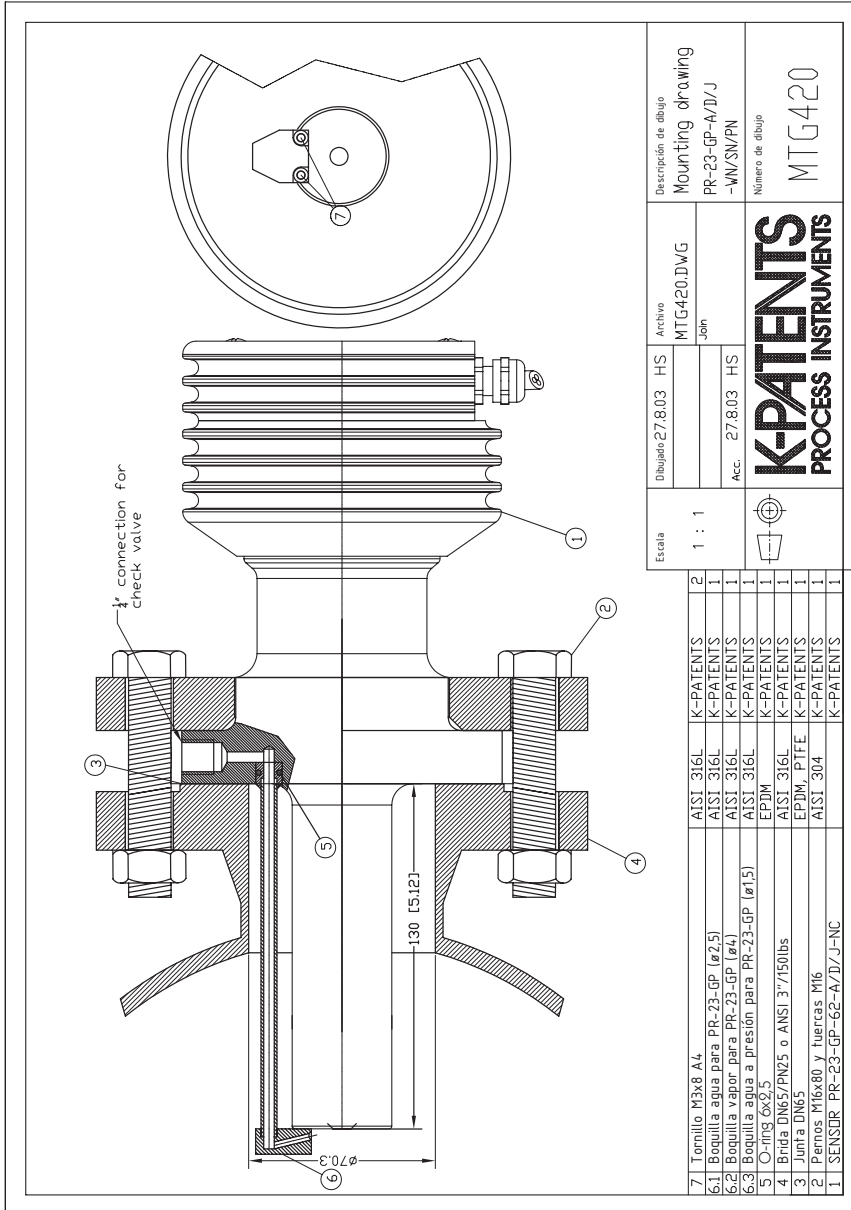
Montaje de la boquilla de lavado para el Refractómetro de proceso PR-23-GP
